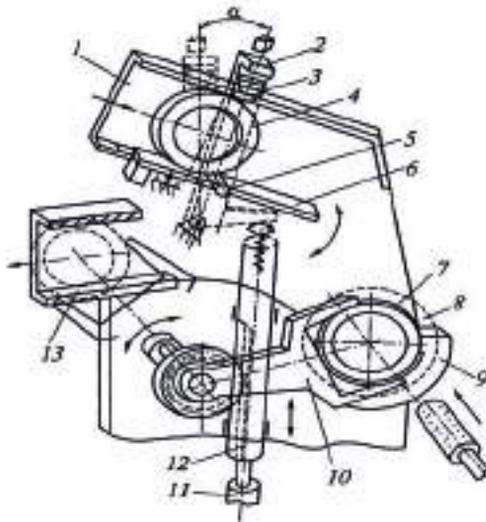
Загрузочное устройство, встроенное во внутришлифовальный автомат: 1 – загрузочный лоток; 2 – рычаг; 3 – упор; 4 – заготовка; 5 – эксцентриковый палец; 6 – планка; 7 – обработанная деталь (кольцо); 8 – магнитный патрон; 9 – радиальная опора; 10 – рука; 11 – гидроцилиндр; 12 – толкатель; 13 – отводящий лоток
